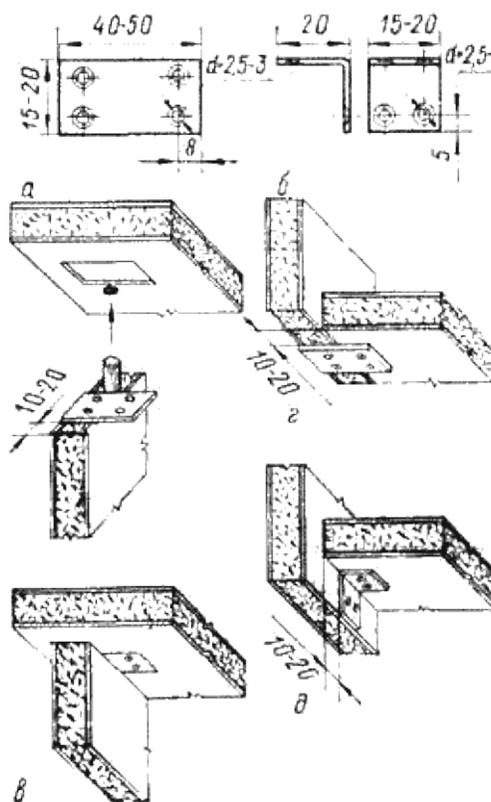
Вспомогательные крепежные детали: а — полосовая стяжка; б — уголковая стяжка; в — крепление крышки к боковой стенке полосовой стяжкой; г и д — крепление днища к боковой стенке полосовой и уголковой стяжкой соответственно
